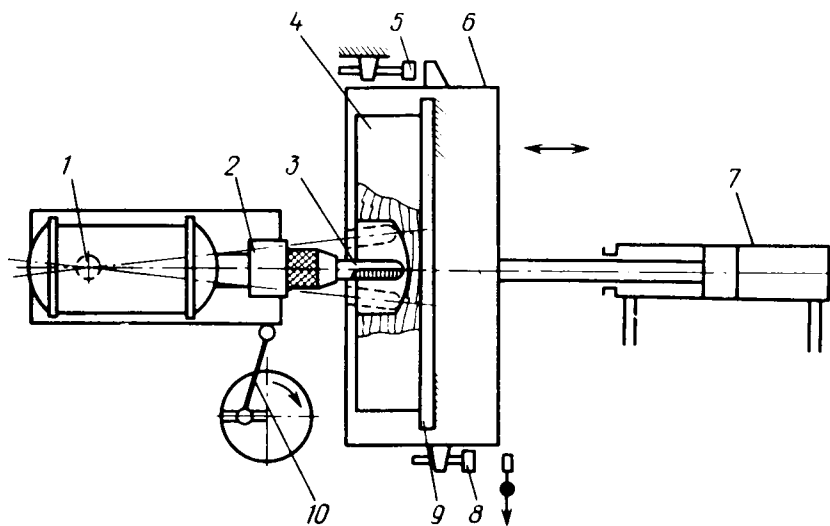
Схема работы сверлильно-пазовального станка СВПА-2:
